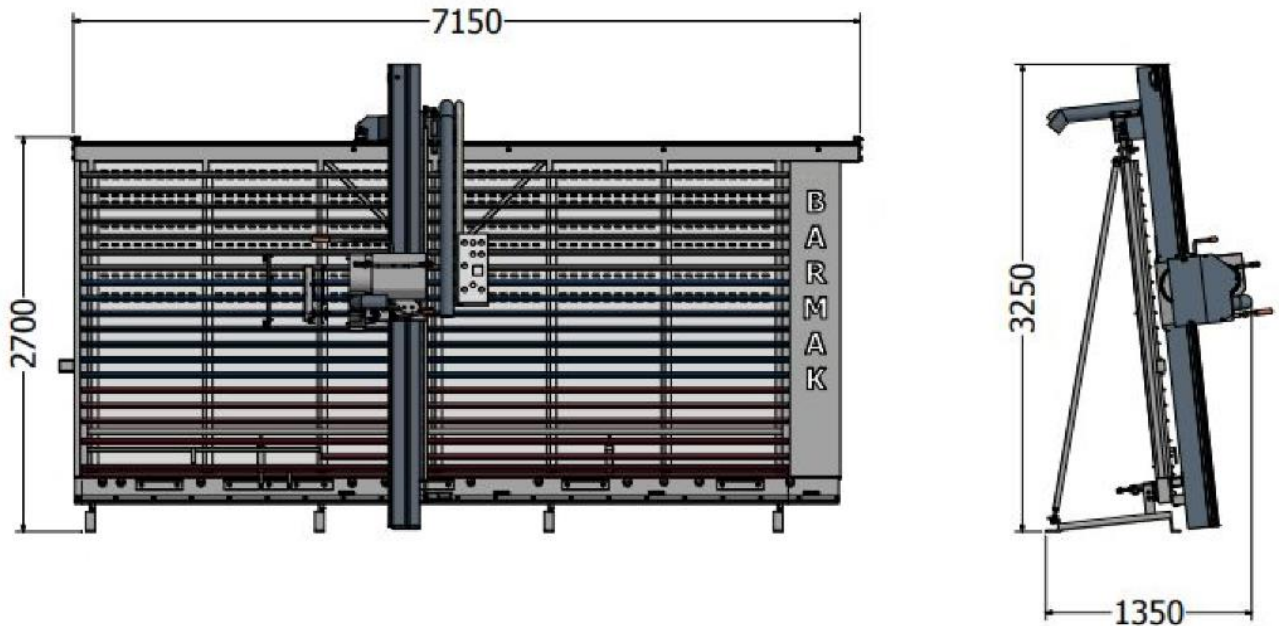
Вертикальний форматно-розкрійний верстат Barmak VM-C7000
